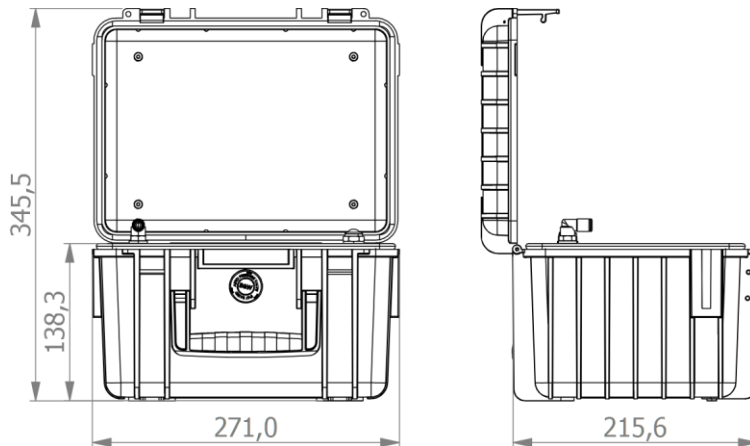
Dimensiones OIL CHECK 500 | versión portátil
